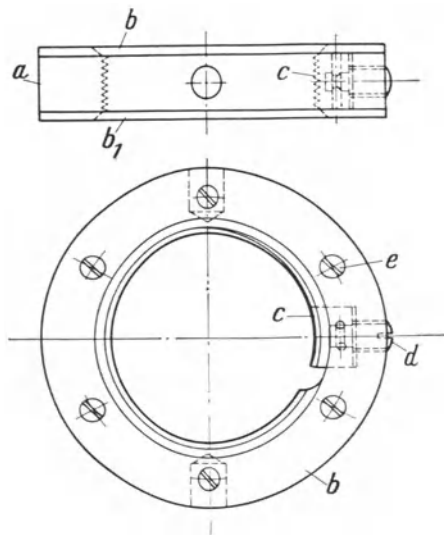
Vorrichtung zum Nachschneiden großer Gewindedurchmesser in Kluppenhalter.
